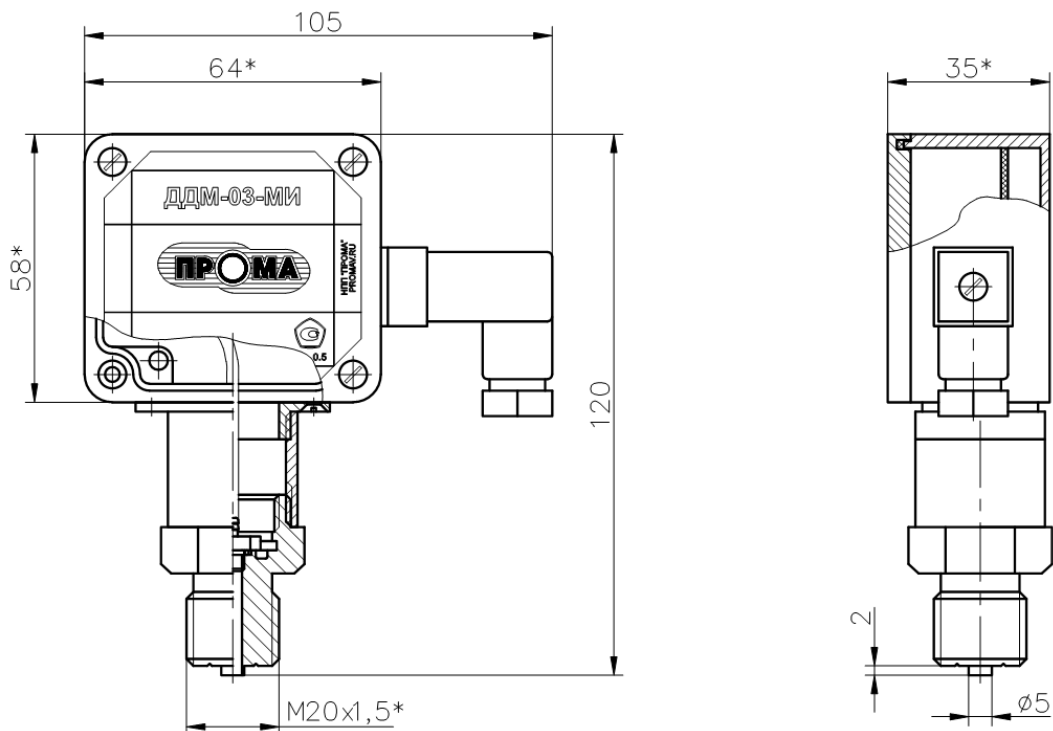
в. Габаритные и присоединительные размеры однопредельного датчика ДДМ-03-ДИ(ДВ,ДИВ,ДА)-МИ-01 без индикатора. Конструктивное исполнение по штуцеру 2.
